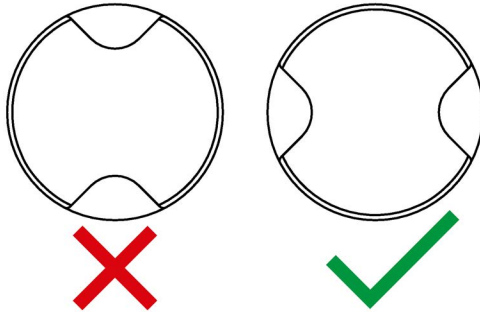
Posición de montaje de la caperuza protectora para selector
